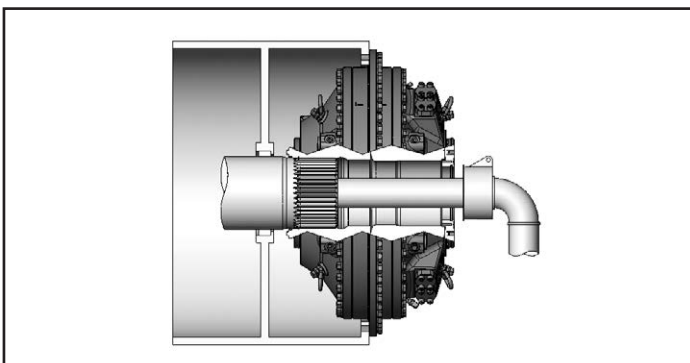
Motor mit Befestigung per Flansch und Vielkeilverzahnung sowie Wellendurchführung zur Kühlung der angetriebenen Maschine.
